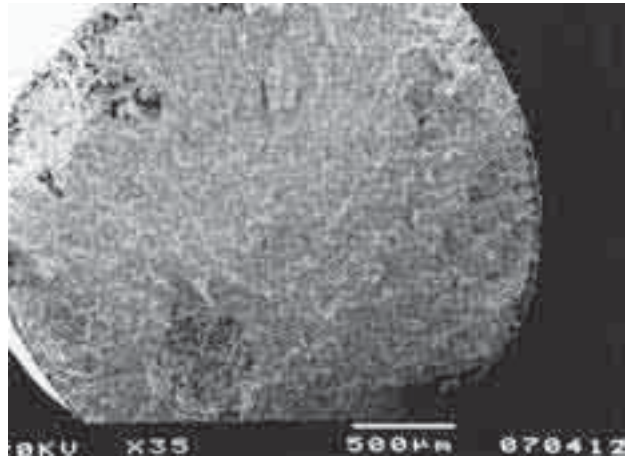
MEV da fratura do corpo-de-prova na condição soldado por brasagem; 35X.
